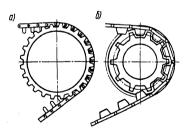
Виды зацепления ведущего колеса с гусеницей: а — цевочное; б — гребневое
